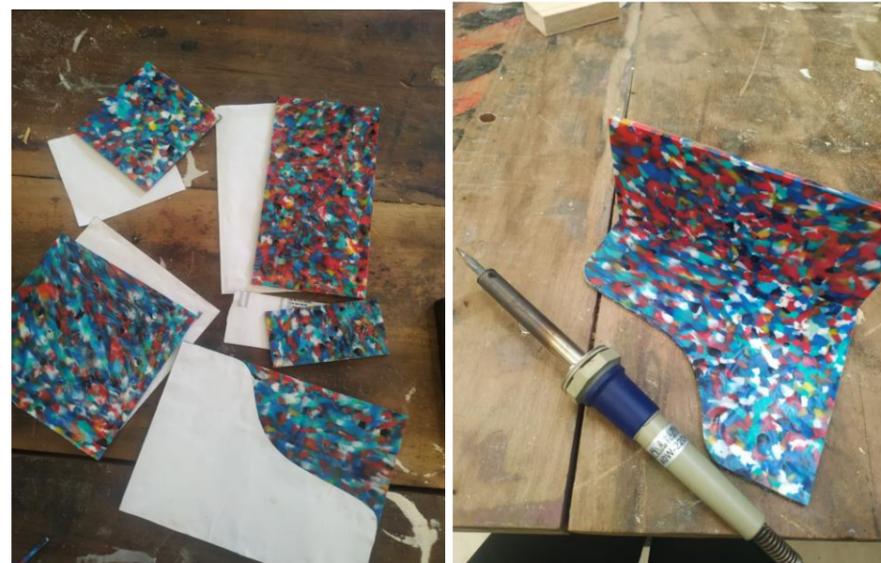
e 7: chapas cortadas de acordo com o molde e montagem com ferro de solda. Fonte: Autoria própria
